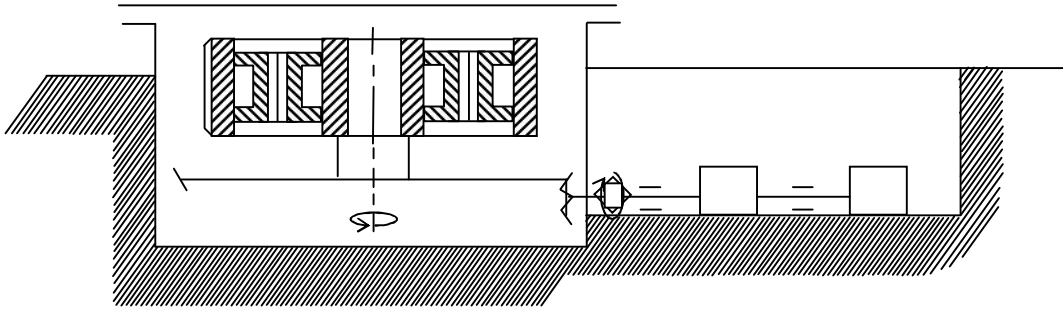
Схема печі з обертовою заготовкою при автоматичній приварці вінця до дисків
